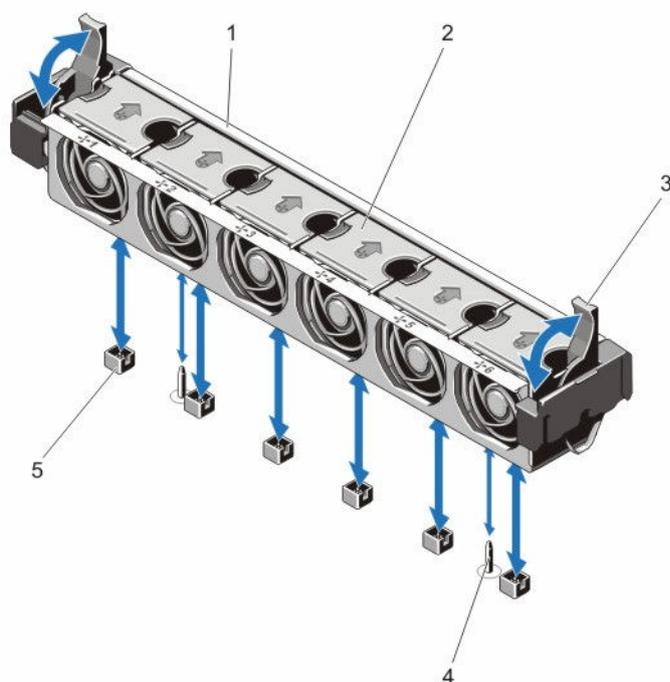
Lüfterbaugruppe entfernen und installieren
